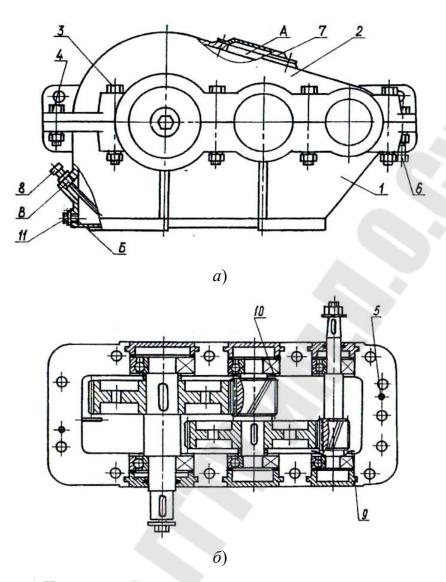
Чертеж цилиндрического двухступенчатого редуктора
